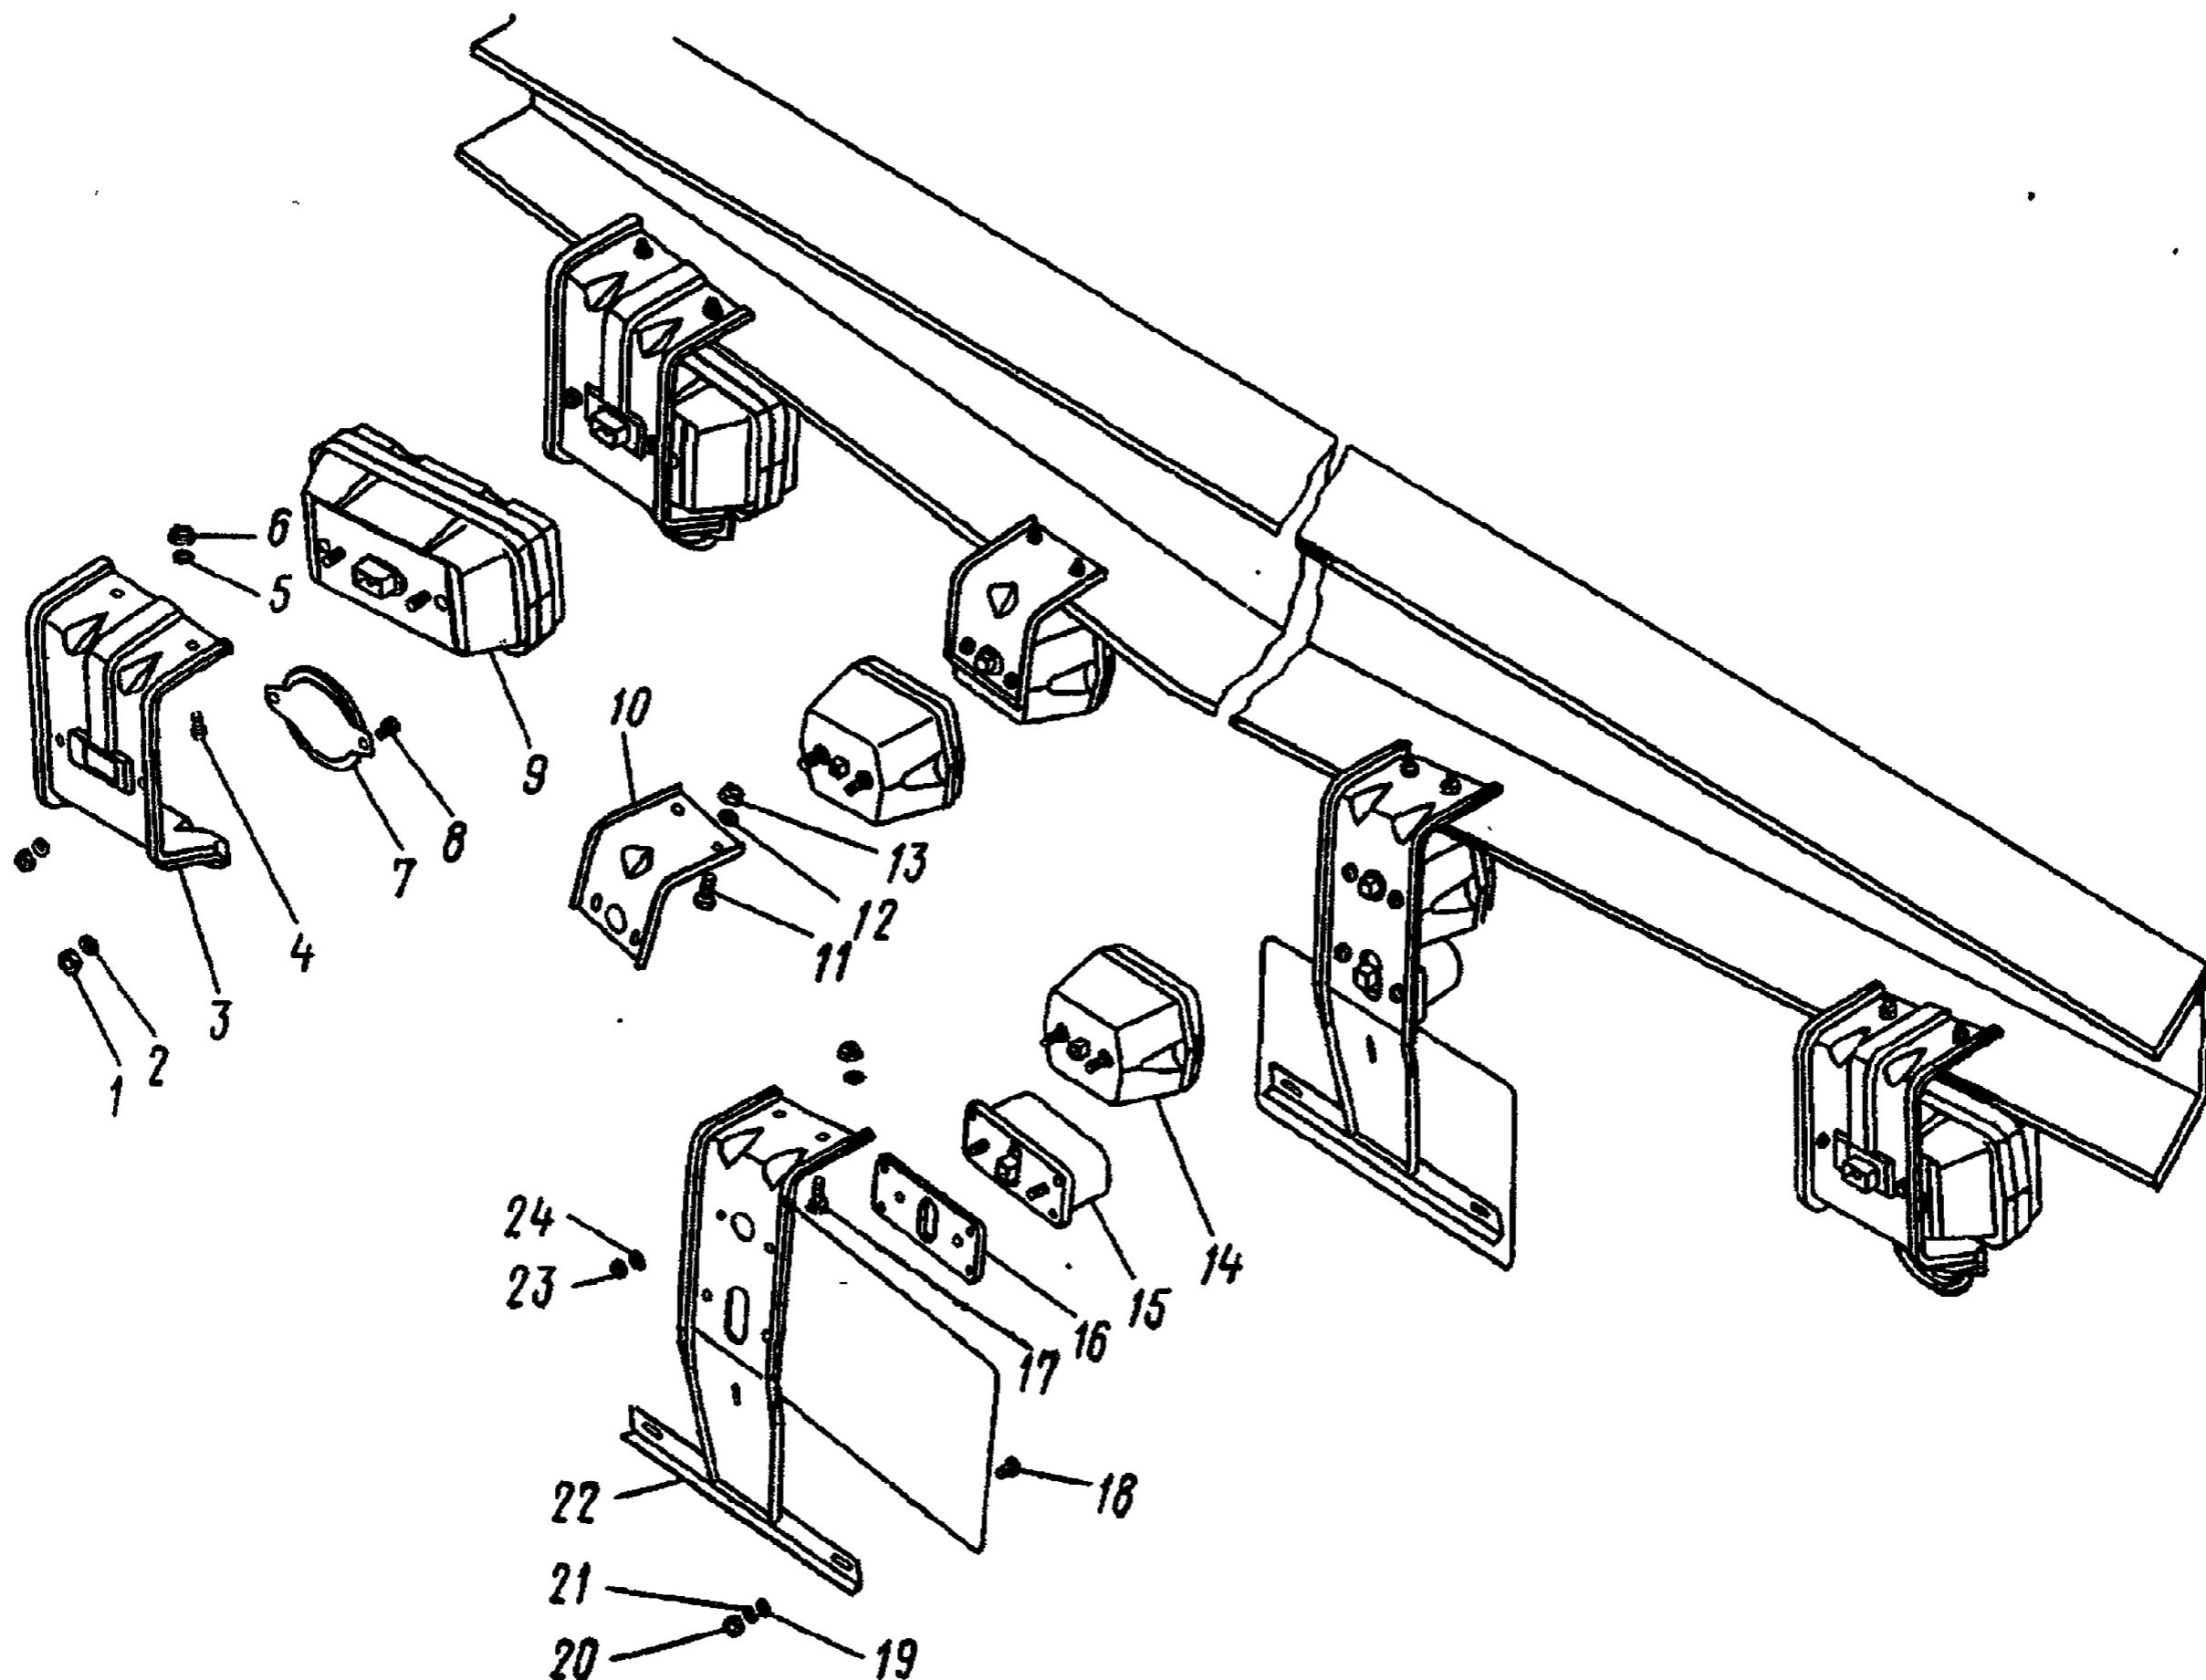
Фонари задние, фонарь освещения номерного знака:
